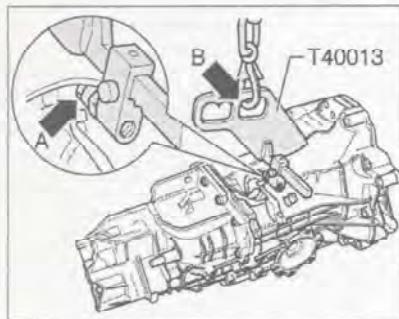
Закрепите приспособление для транспортировки T40013 в отверстии корпуса коробки передач (стрелка A). Сдвиньте механизм приспособления до упора. Подцепите краном устройство для транспортировки за вторую проушину (стрелка B).
